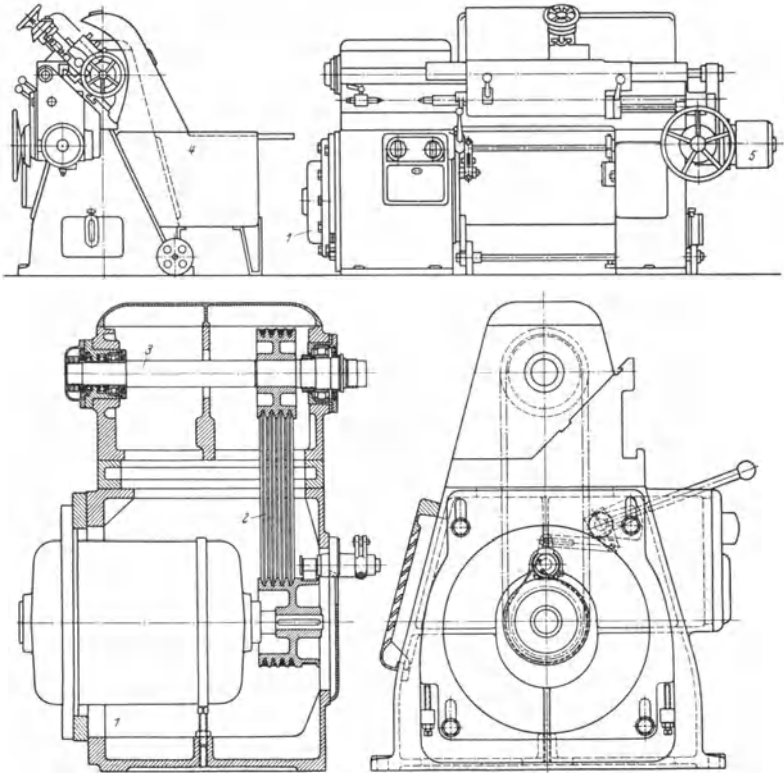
u. 36. Fließspindrehbank der Magdeburger Werkzeugmaschinenfabrik.
